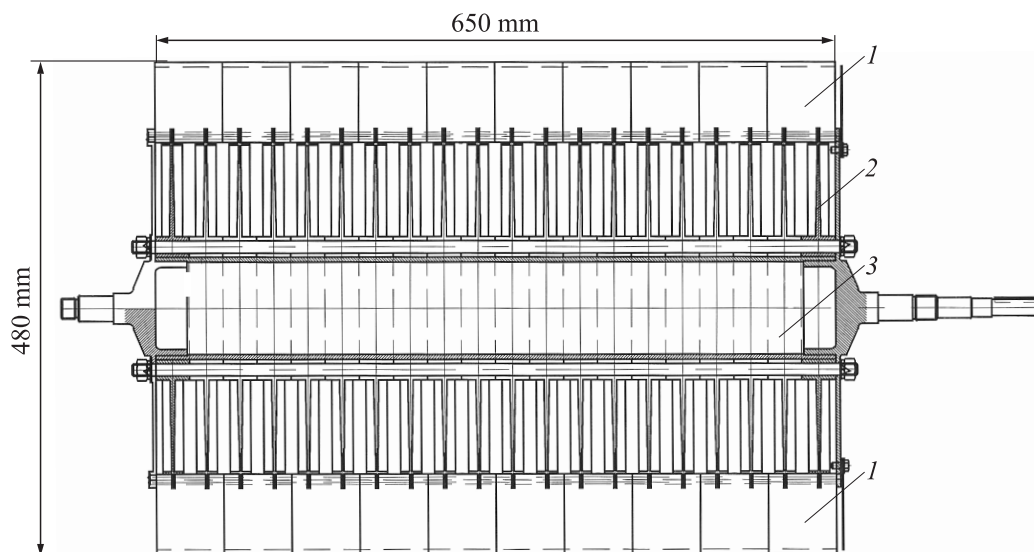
Общий вид ротора механического монохроматора. 1 — поглощающие пластины, 2 — диски для установки пластин, 3 — труба для крепления дисков.
